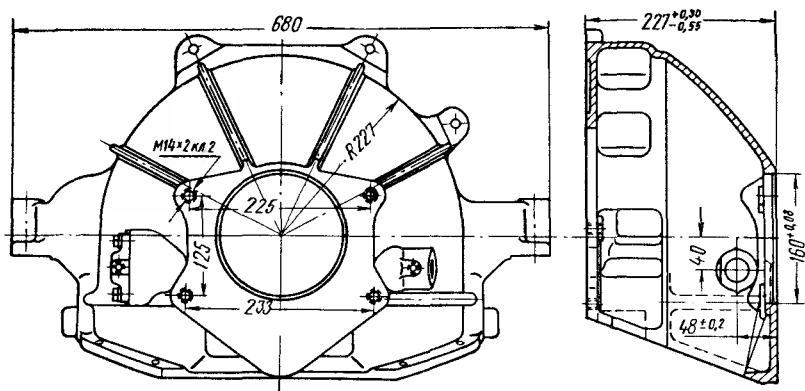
Картер сцепления двигателя ЗИЛ-130
